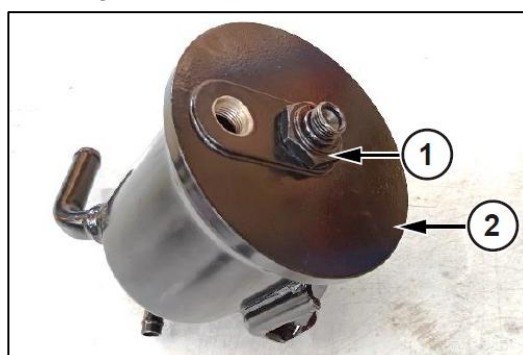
DESSERRER L'ÉCROU DE FIXATION DU COUVERCLE ET DÉPOSER CE DERNIER
